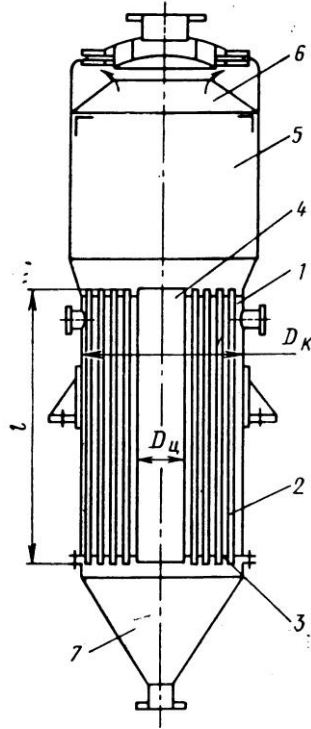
Випарний апарат з внутрішньою циркуляційною трубою: 1– гріюча камера; 2– нагрівальні трубки; 3– трубні решітки; 4– циркуляційна труба; 5– сепаратор; 6–краплевідокремлювач; 7– днище
